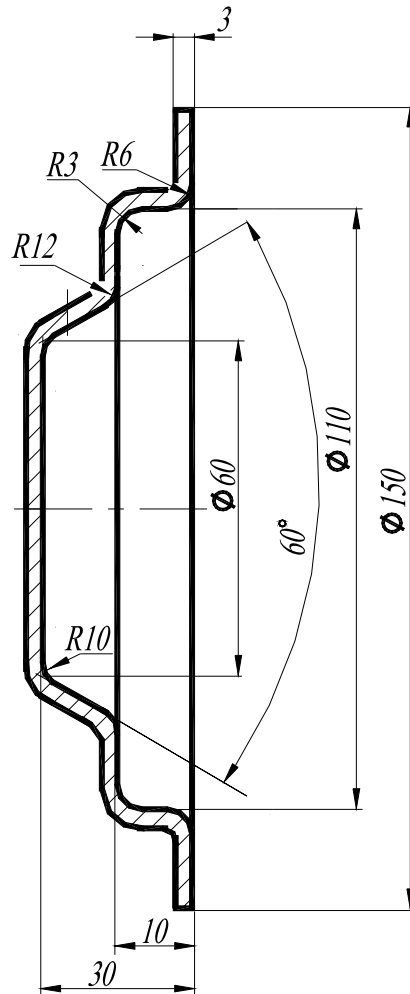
Нанесение размеров детали, изготовленной холодной штамповкой, по пуансону
